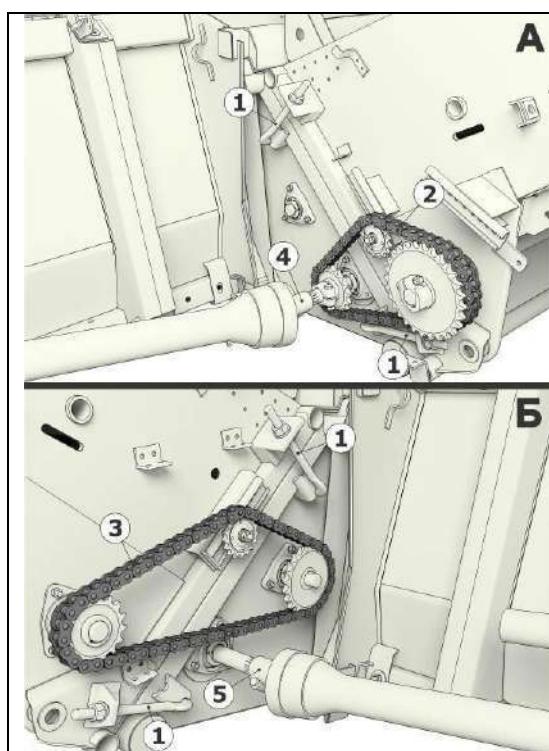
Установка проставки на приспособления ПСП-810-03/-39
